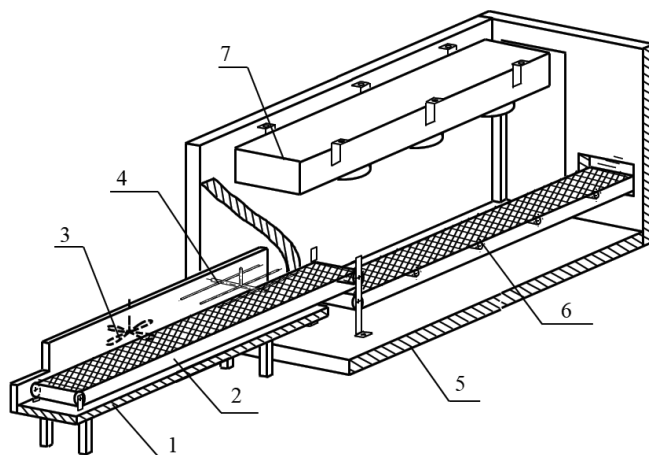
Эскизный проект двухкорпусной скороморозильной установки: 1 — корпус азотного замораживания; 2, 6 — конвейеры; 3 — вентилятор; 4 — коллектор с форсунками; 5 — корпус воздушного замораживания и выравнивания температуры; 7 — воздухоохладитель
